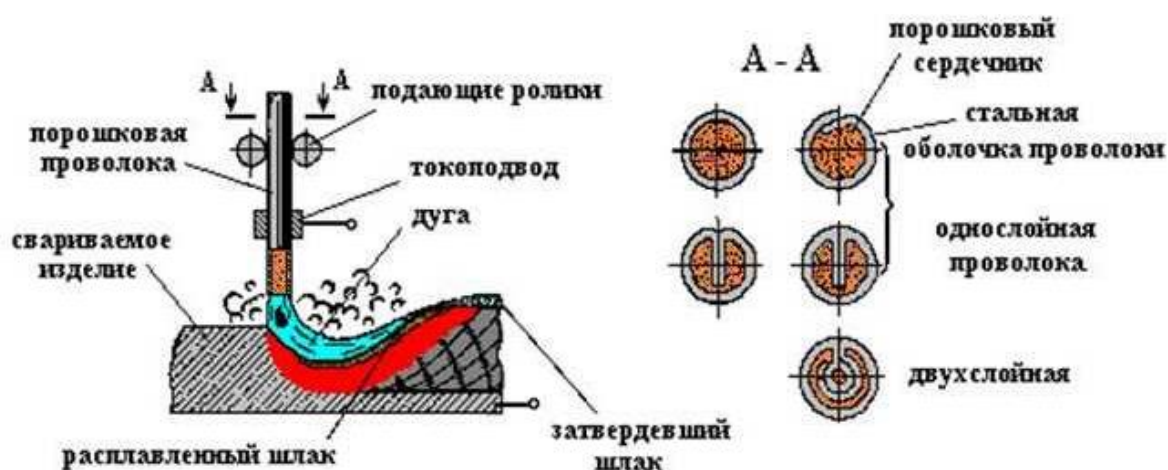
Схема выполнения сварки самозащитной проволокой
